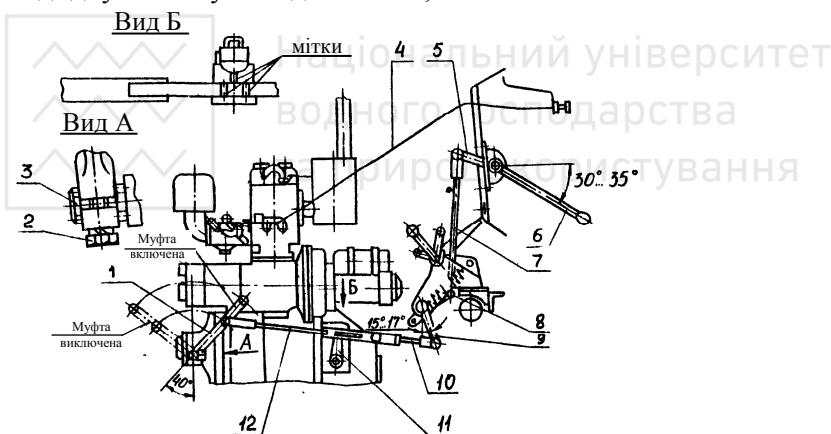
Регулювання керування муфтою зчеплення і механізму включення пускової шестерні редуктора пускового двигуна: 1 - важіль муфти зчеплення редуктора; 2 – болт; 3 - валик; 4 - тяга керування повітряною заслінкою 5, 8, 9, 11 - важіль; 6 - рукоятка керування; 7, 10, 12 – тяга
